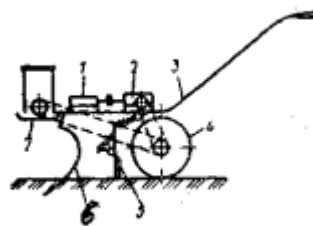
Комбинированный почвообрабатывающий агрегат
